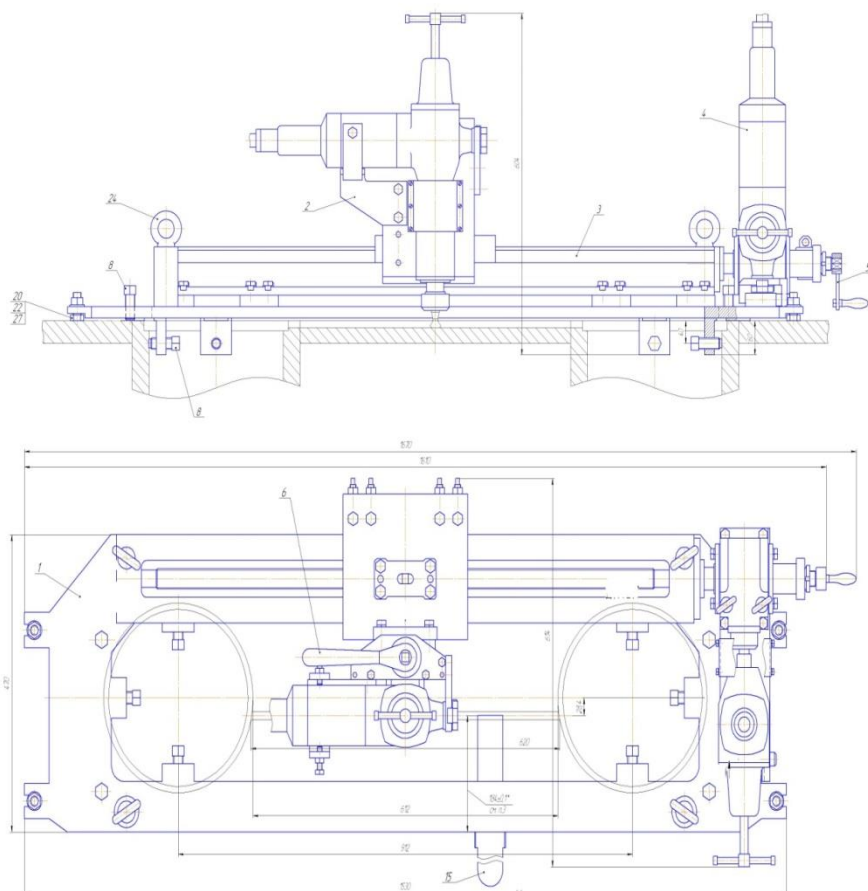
Компонування OXZCv мобільного портативного фрезерного верстату
